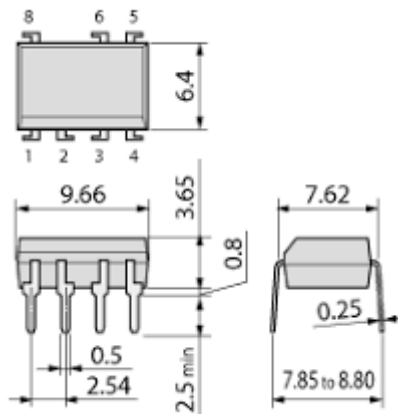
Габаритні розміри мікросхемиLM358
